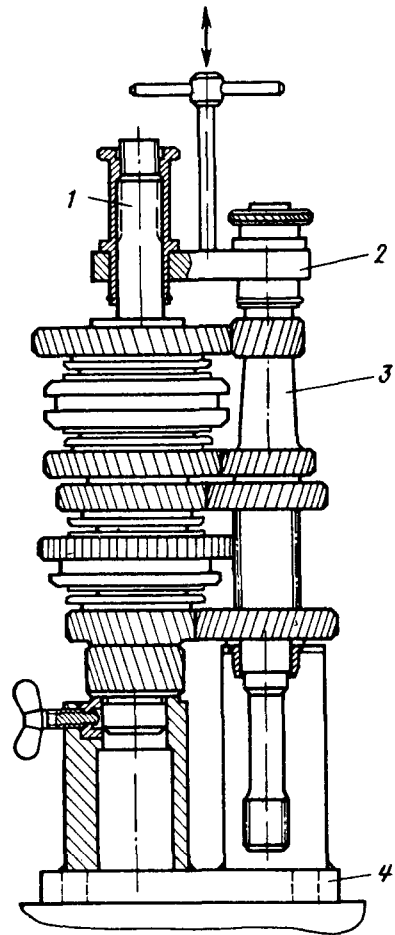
Ведомый и ведущий валы с приспособлениями для их снятия и установки:
